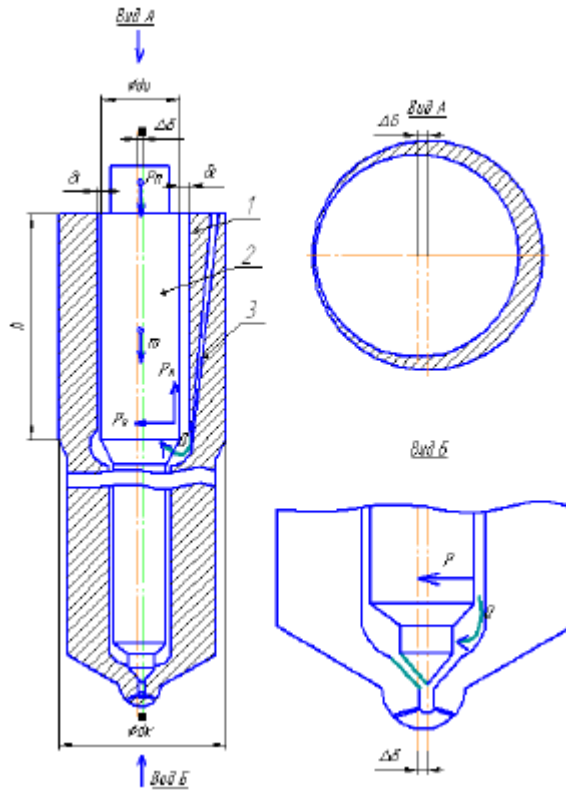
Схема сил, що діють на голку розпилювача : 1 - корпус; 2 - голка; 3 - канал подачі палива.
